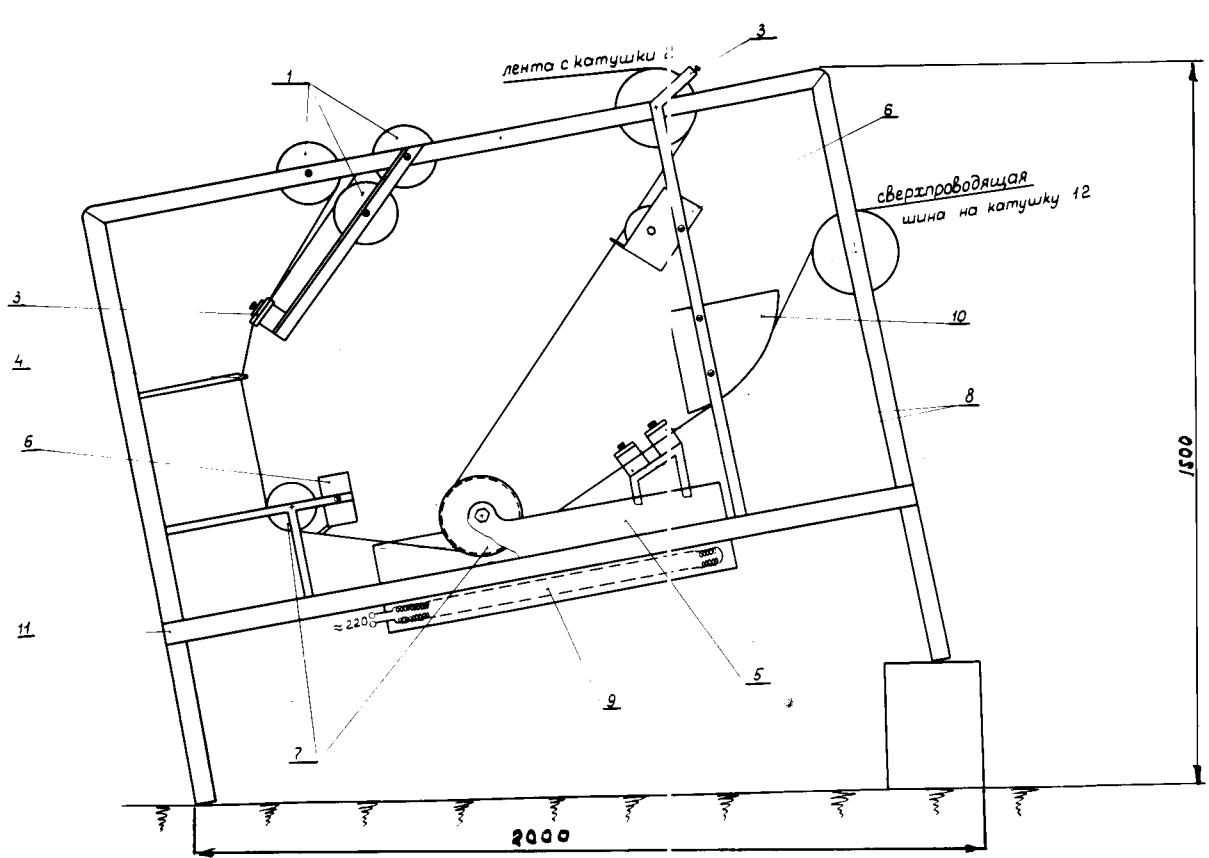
Схема установки для изготовления сверхпроводящей шины методом пайки.
